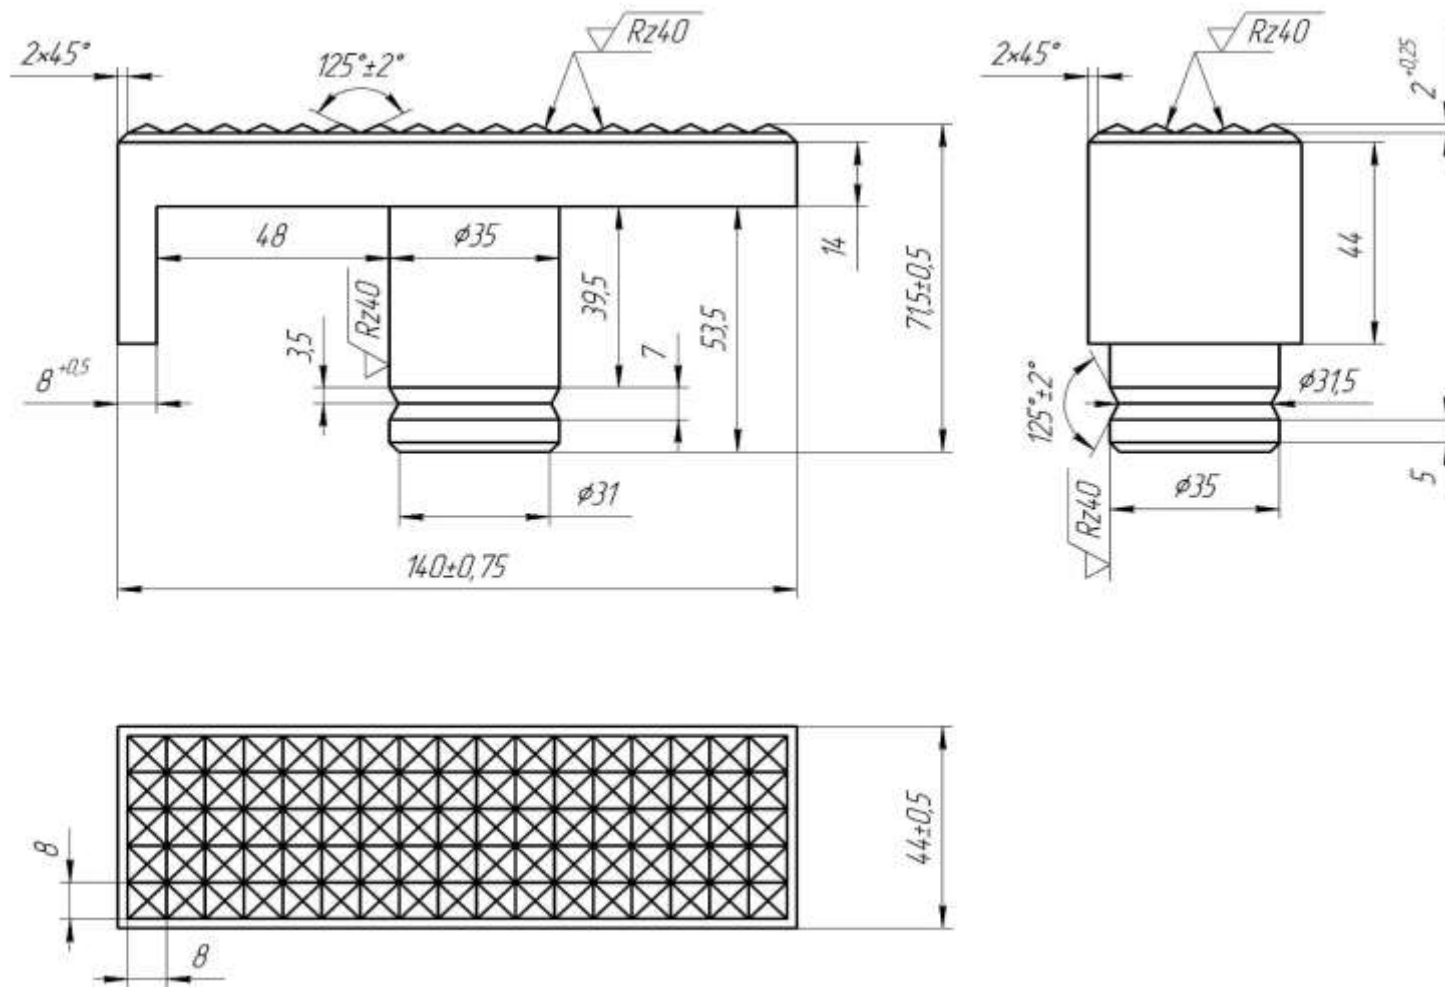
Затискний пристрій шиномонтажного стенда
